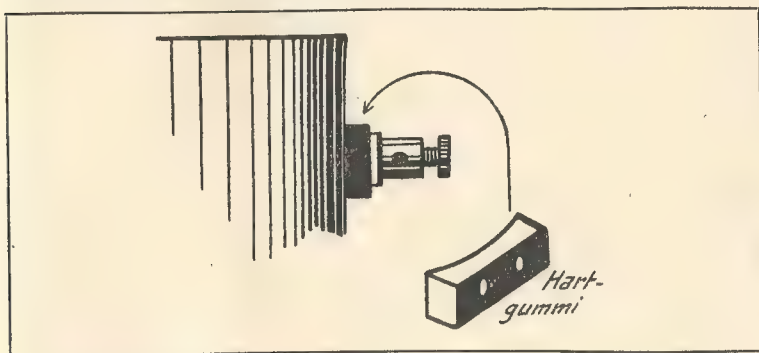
Wie die Anschlußklemmen auf der Außenwand des Magnetgehäuses befestigt werden.
